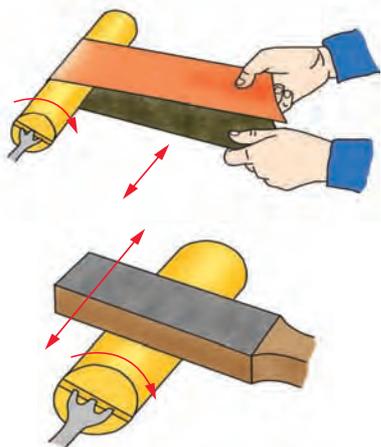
Шлифование поверхности: шлифовальной шкуркой (вверху) и бруском со шлифовальной шкуркой (внизу)
